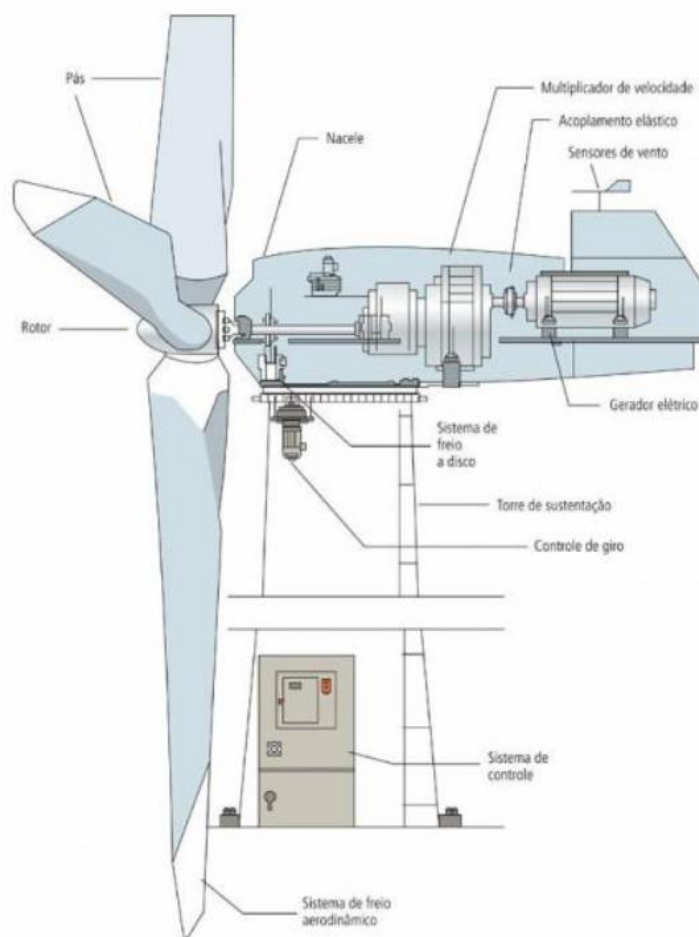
Representação das partes de uma turbina de eixo horizontal [5]
